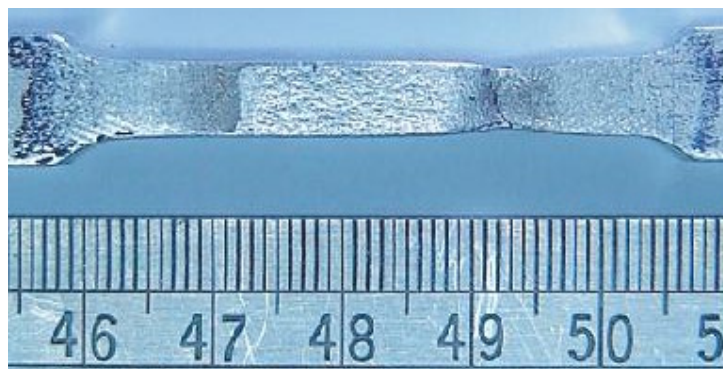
Ruptura ao lado do cordão de solda MIG.
